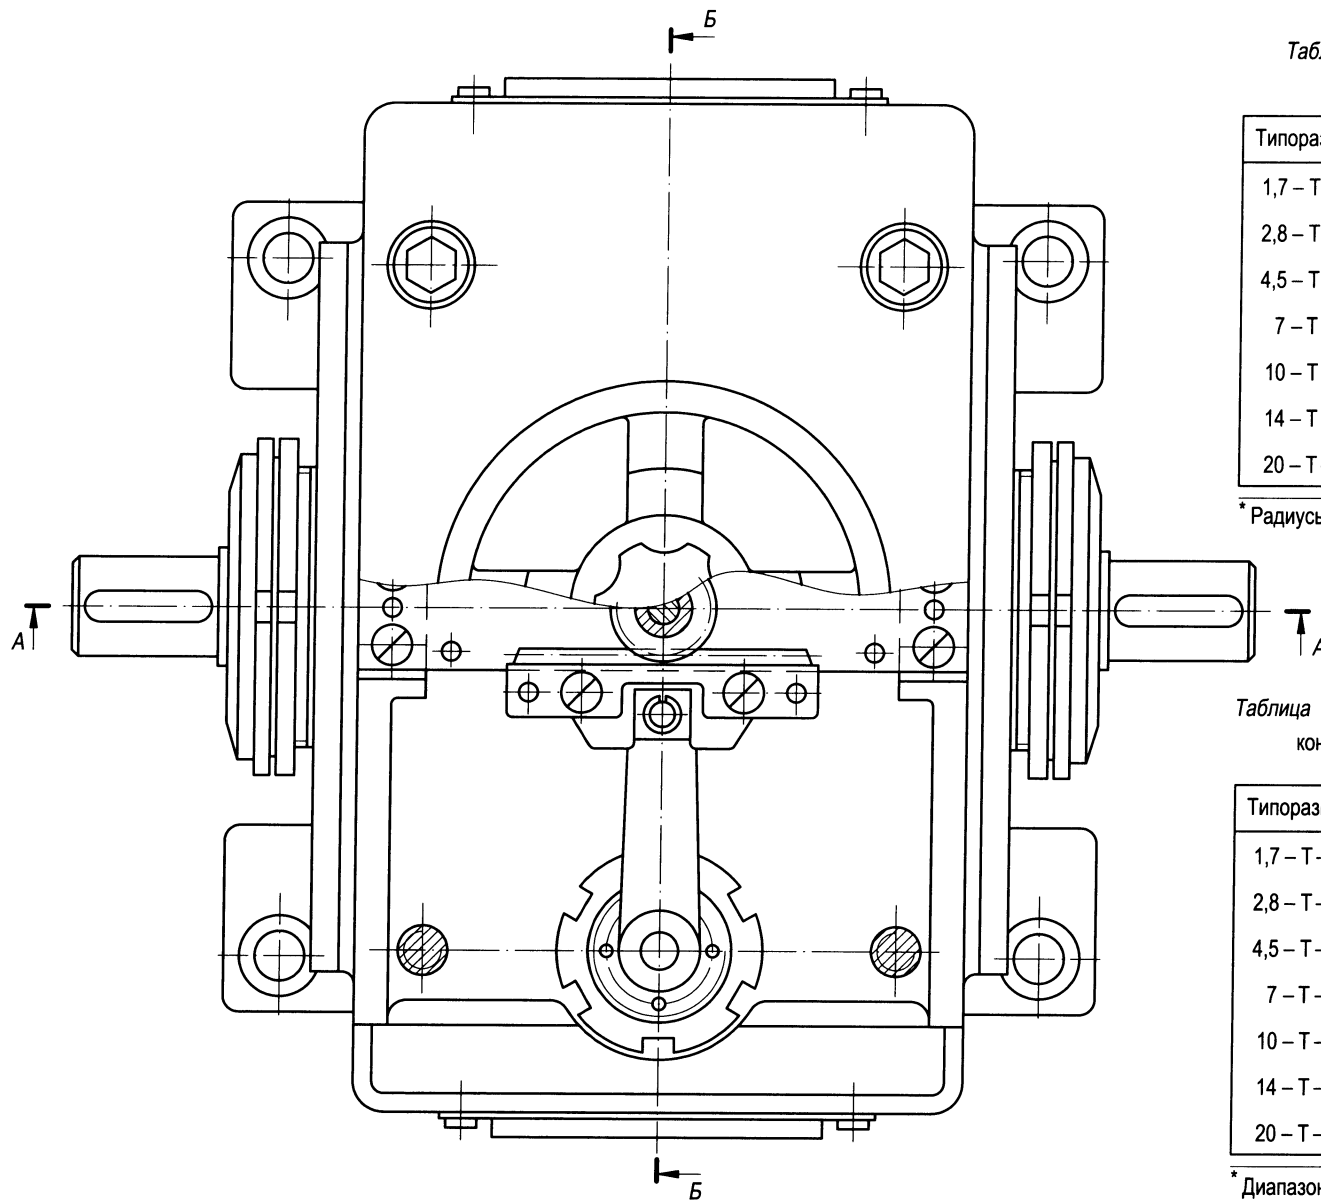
Торковый вариатор конструкции ЦНИИТМАШ (начало)
